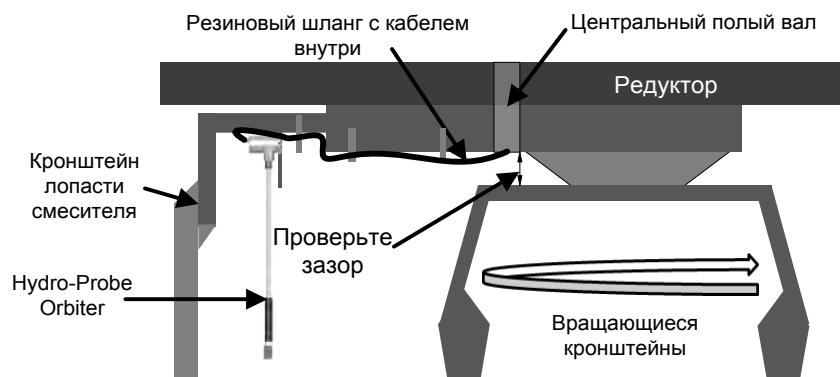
Проверка зазора между вращающимся кронштейном и редуктором смесителя
